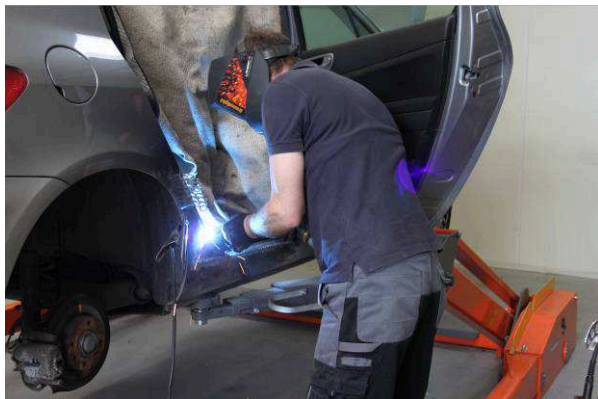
Verschließen aufgerissener Löcher mittels Schweißen
